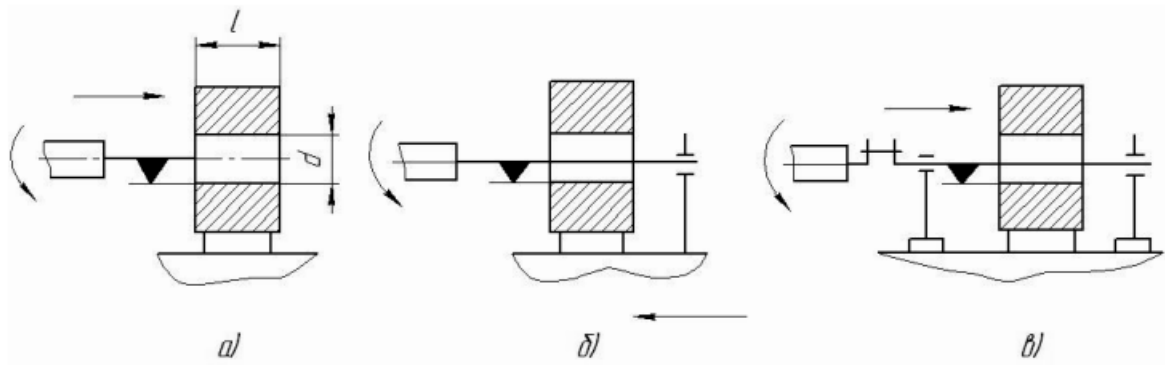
Теоретичні схеми розточування на розточних верстатах:
